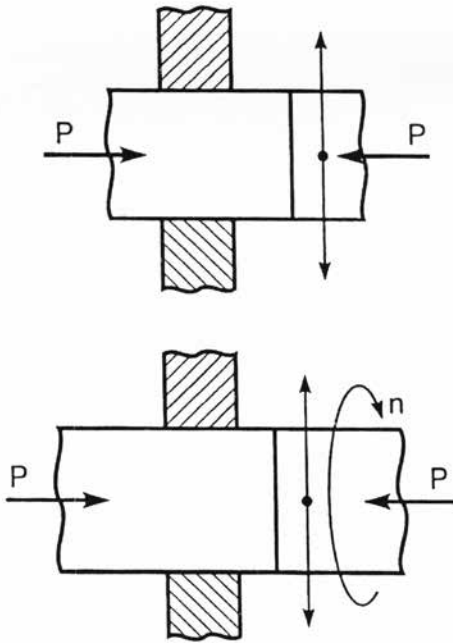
Схема вибративной (линейной) СТ: а – колебательные движения одной свариваемой детали относительно другой; б – колебательные движения одной свариваемой детали с вращением
